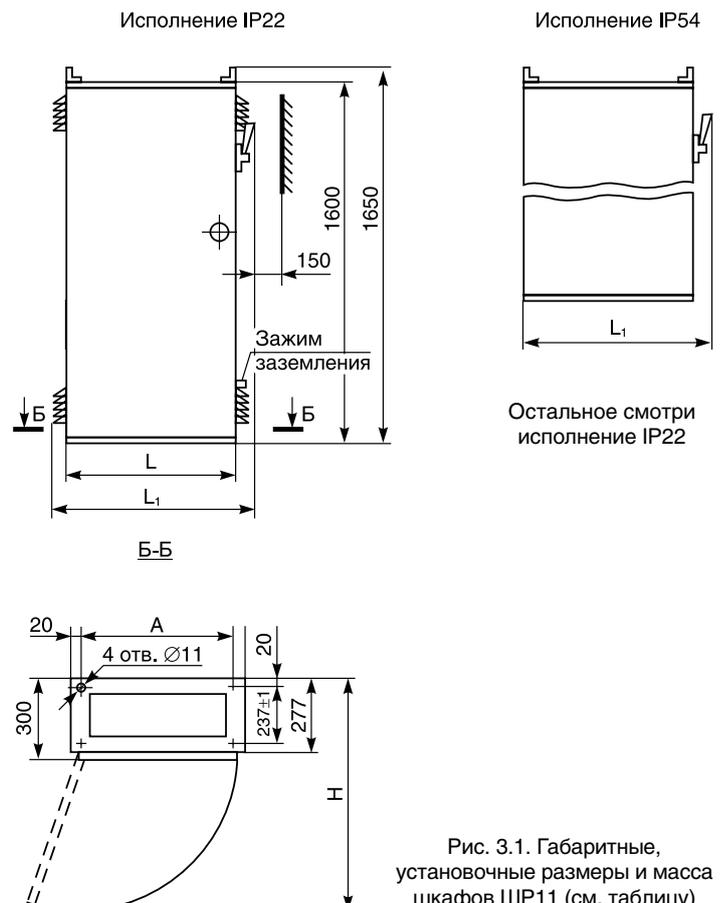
Габаритные, установочные размеры и масса шкафов ШП11 (см. таблицу)
